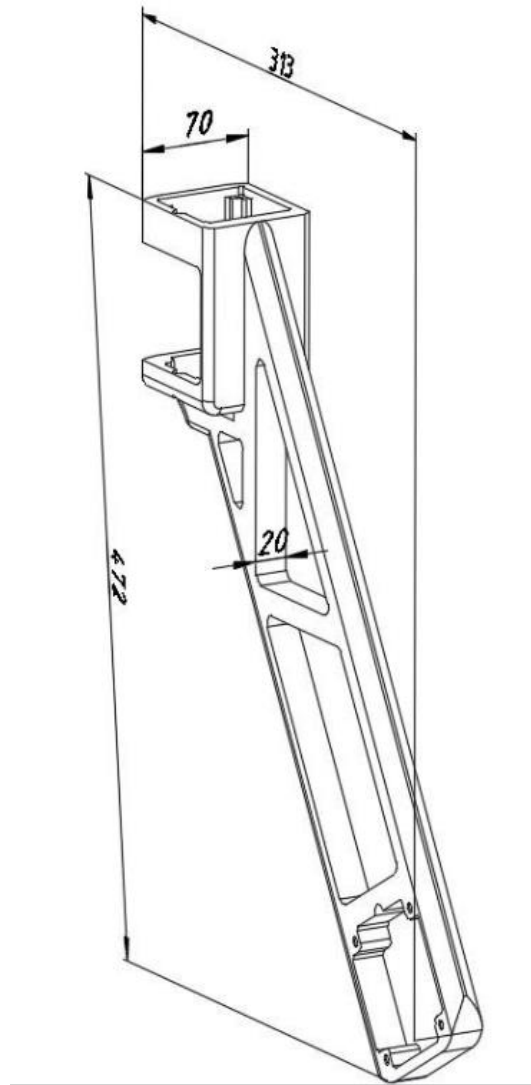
Габаритні розміри елемента важіля верхньої частини крокуючої ланки
